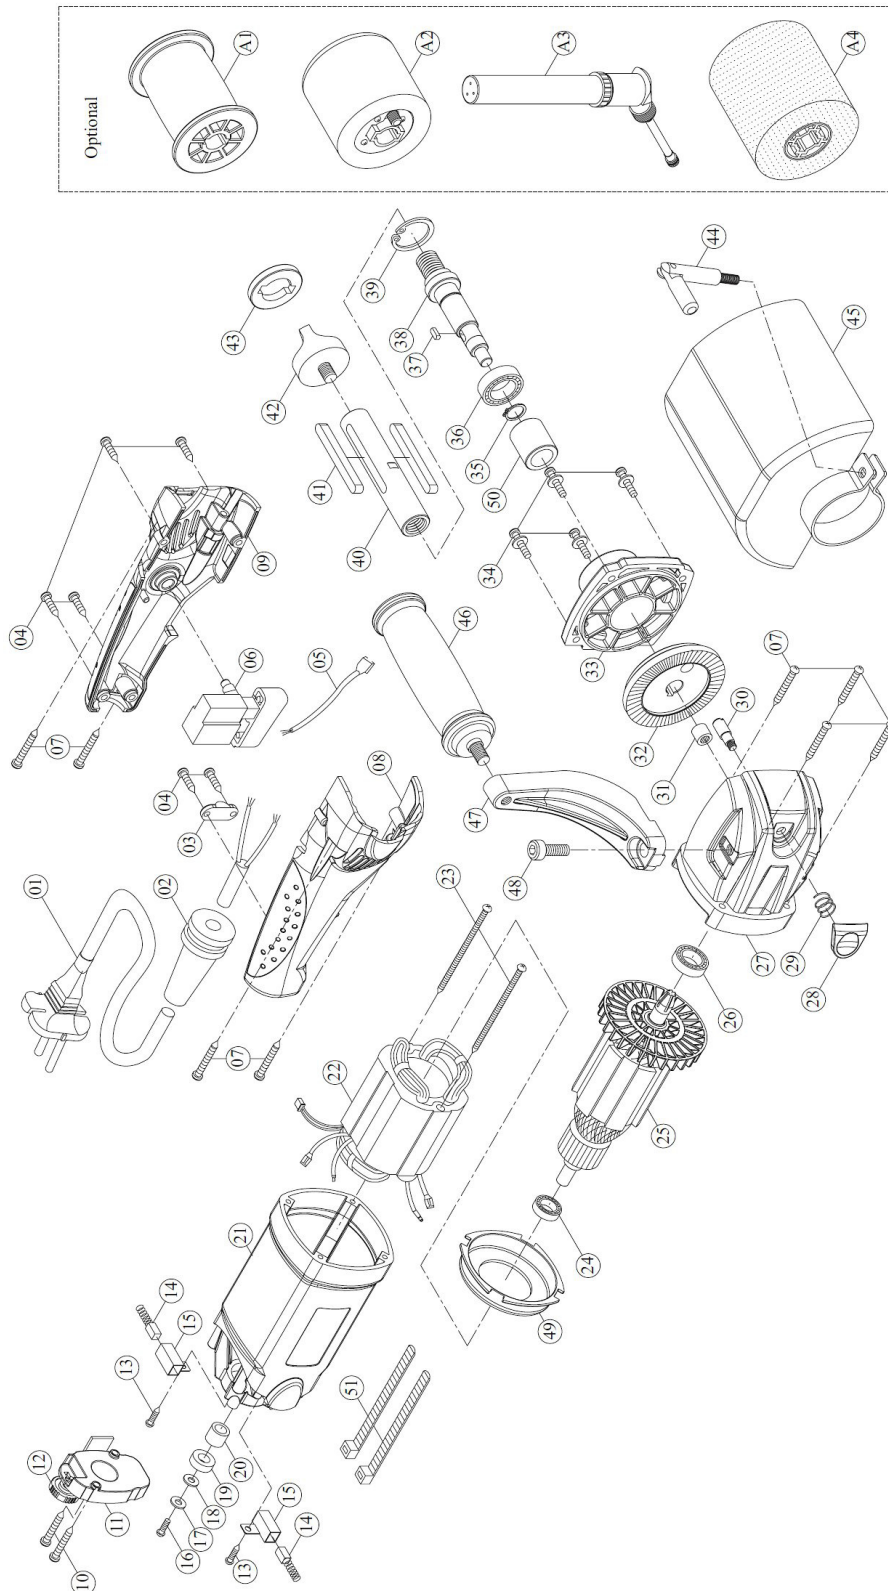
Plano de piezas de repuesto para la máquina de acabado satinado SM 100
